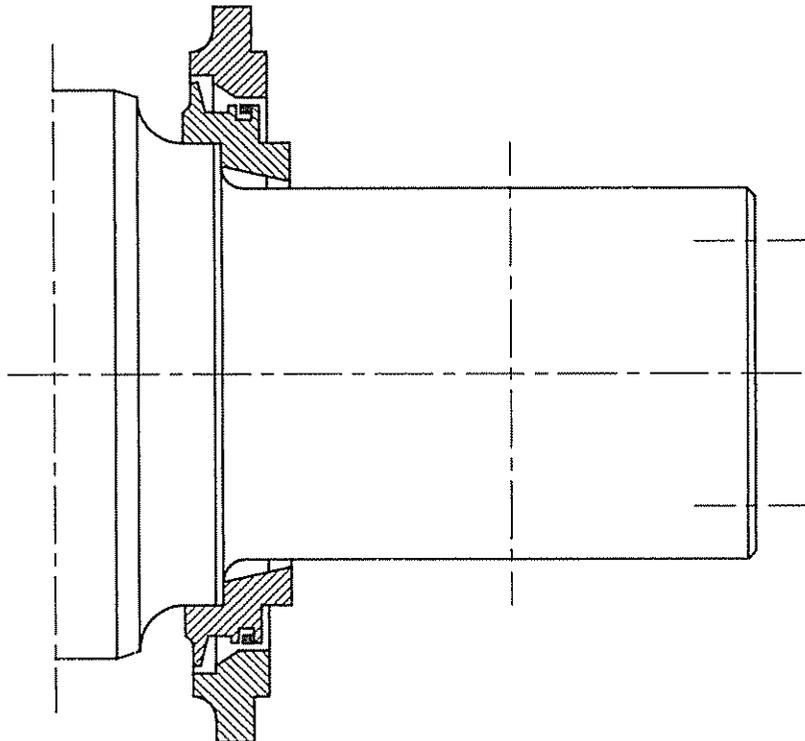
Pressa idraulica per montaggio-smontaggio boccole
